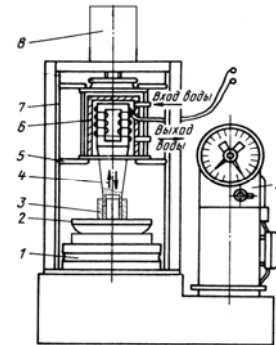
Схема установки для прессования изделий из политетрафторэтилена с наложением ультразвуковых колебаний:
